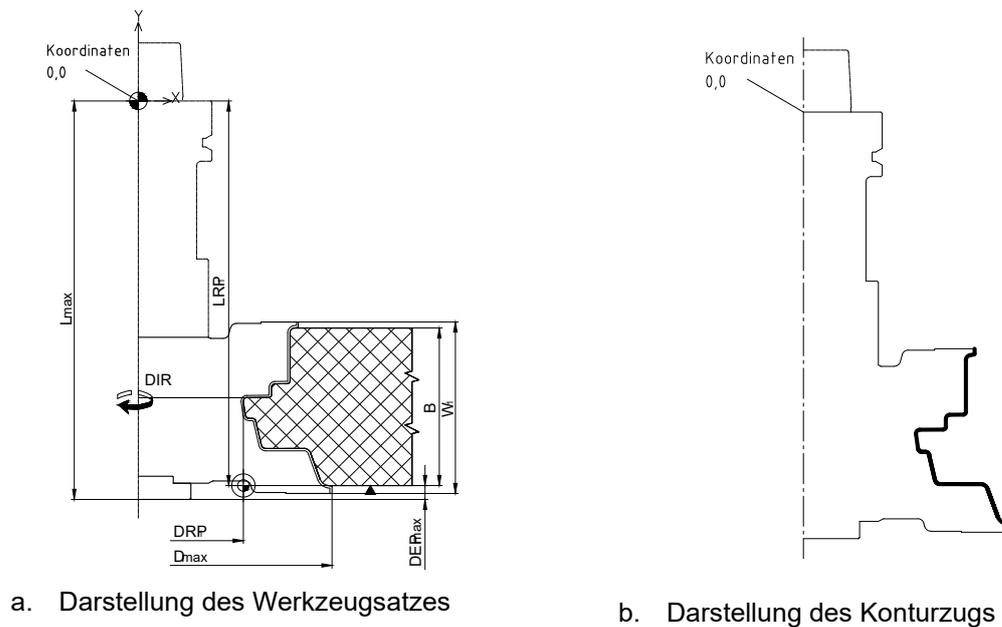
Werkzeugsatz in einer Aufnahme oder auf einer Motorspindel.
